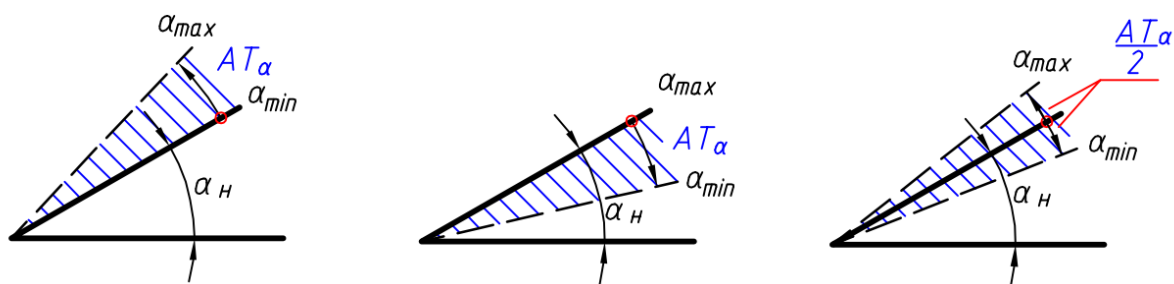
Расположение допуска на угловые размеры относительно номинального значения угла:
